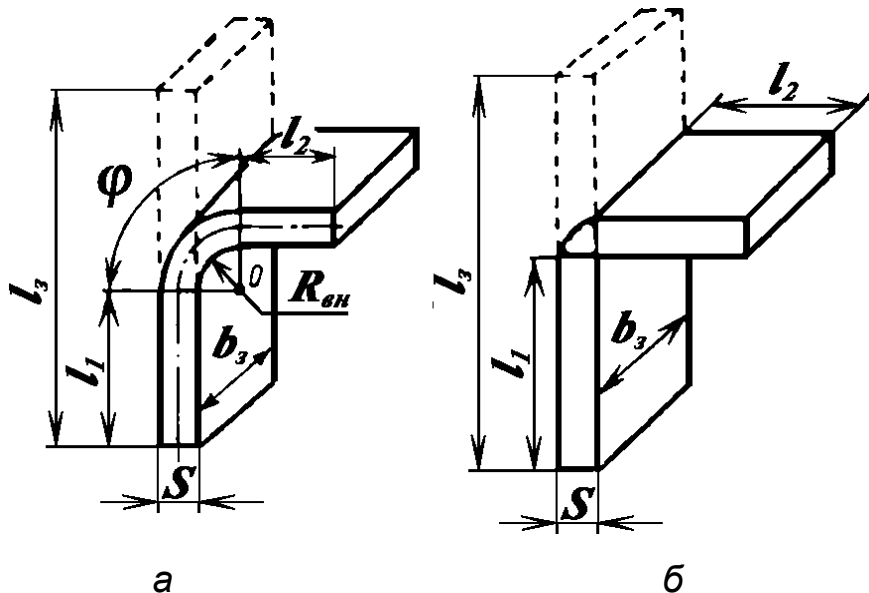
Розрахунок довжини заготовки під час згинання:
